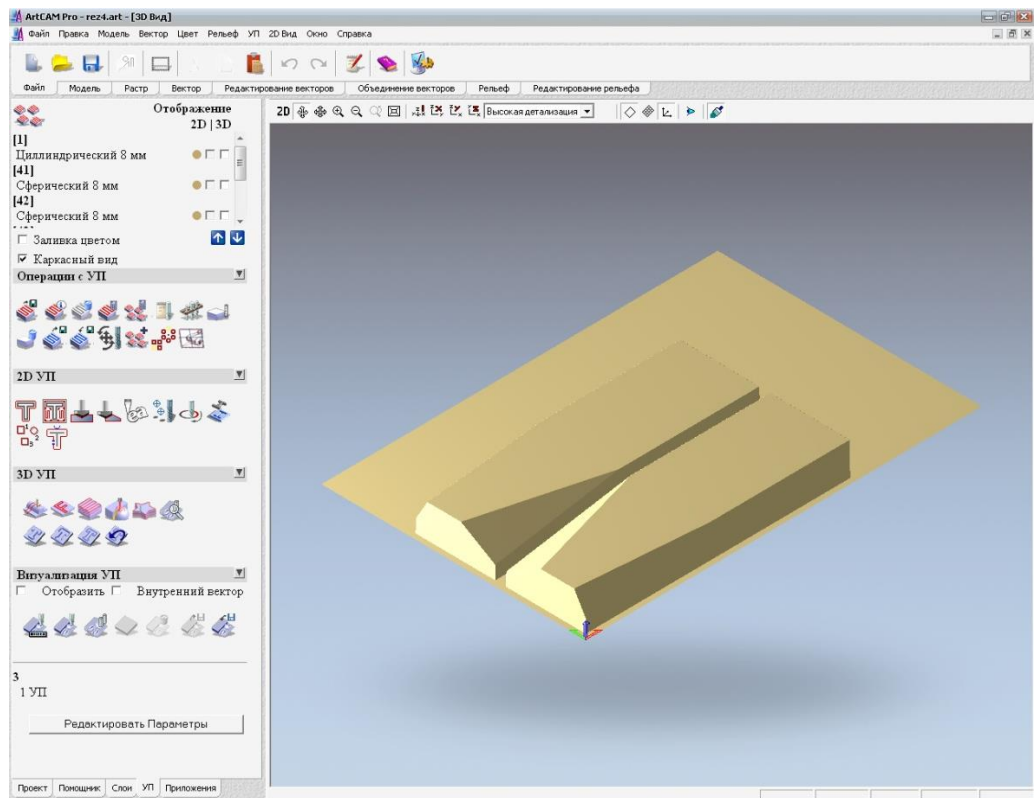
Деталі, що отримуються з четвертої заготовки, розташовані на робочій площині
